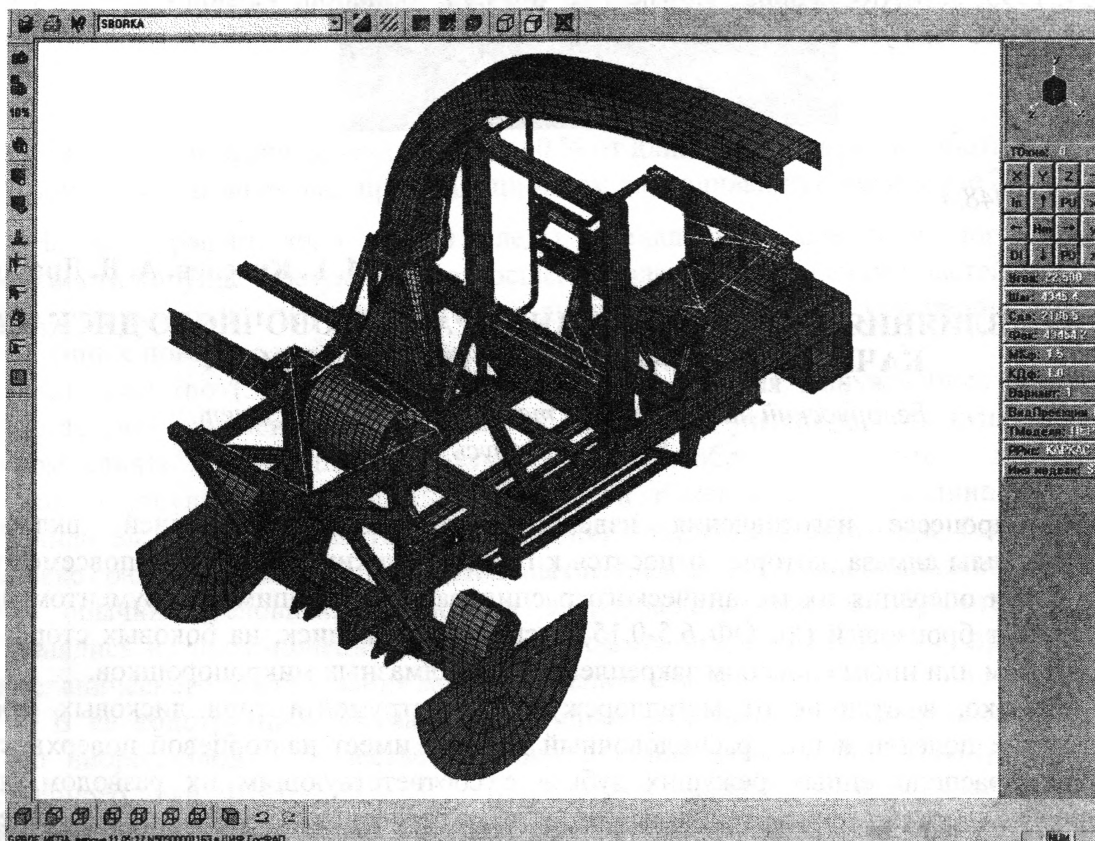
КЭМ несущей конструкции кормоуборочного комбайна Полесье-800.
